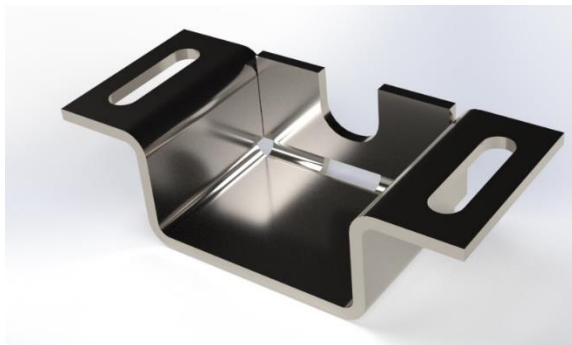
Модель деталі, створеної в середовищі модуля Sheet Metal.
